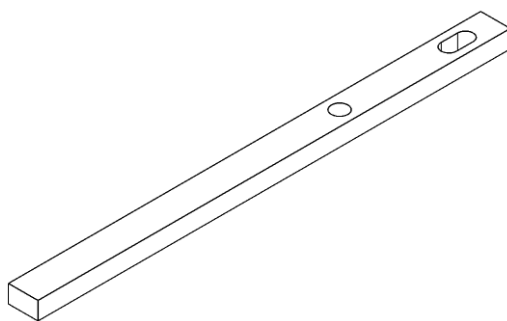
Perspectiva isométrica “Apoio corte CM M1 VF”.
